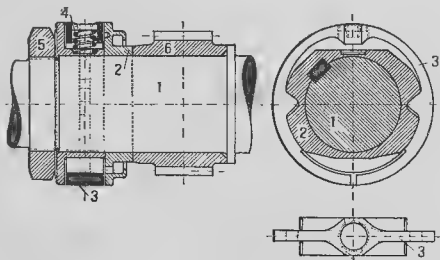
Предохранительный выключатель турбины АЭГ.
